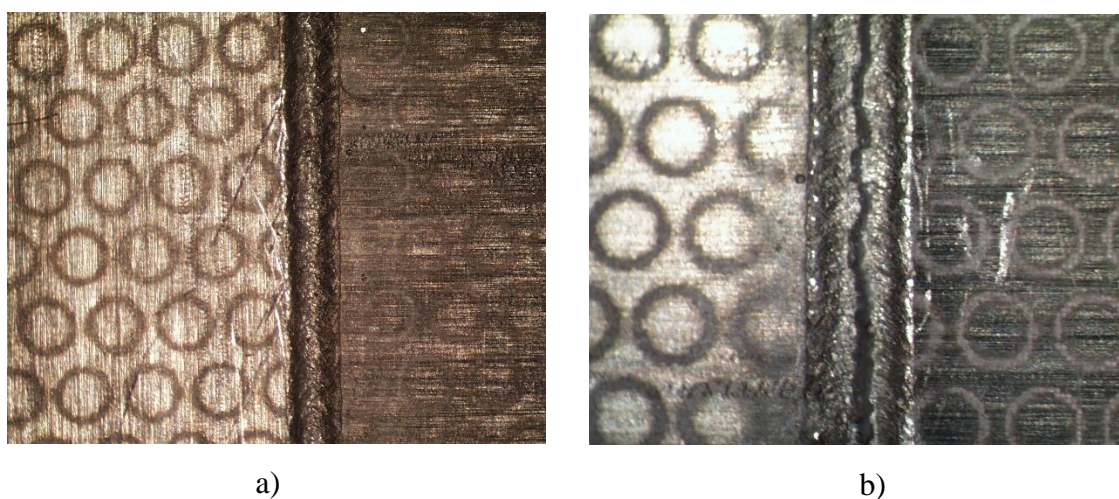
Dimensão do cordão de soldadura antes (a) e após fecho (b) do cerra-chapas.
